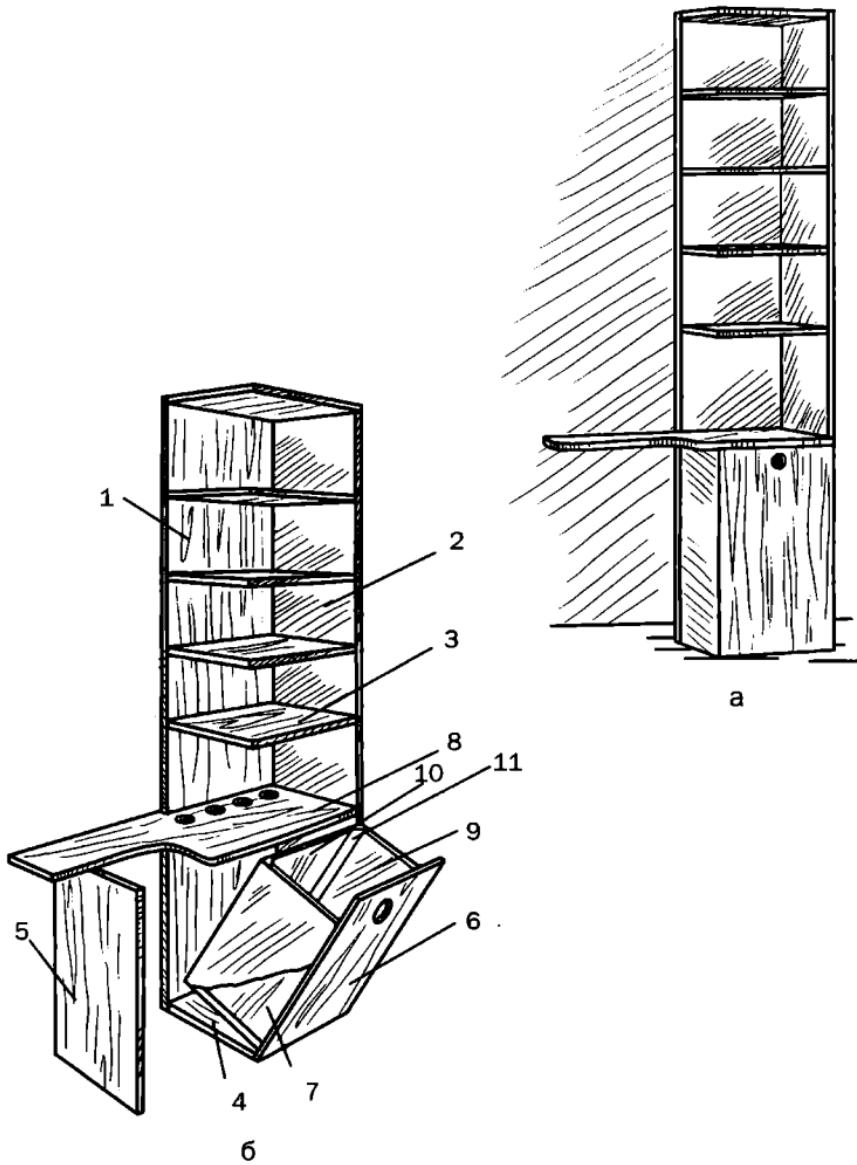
Стеллаж-башня: а — общий вид; б — схема сборки:
